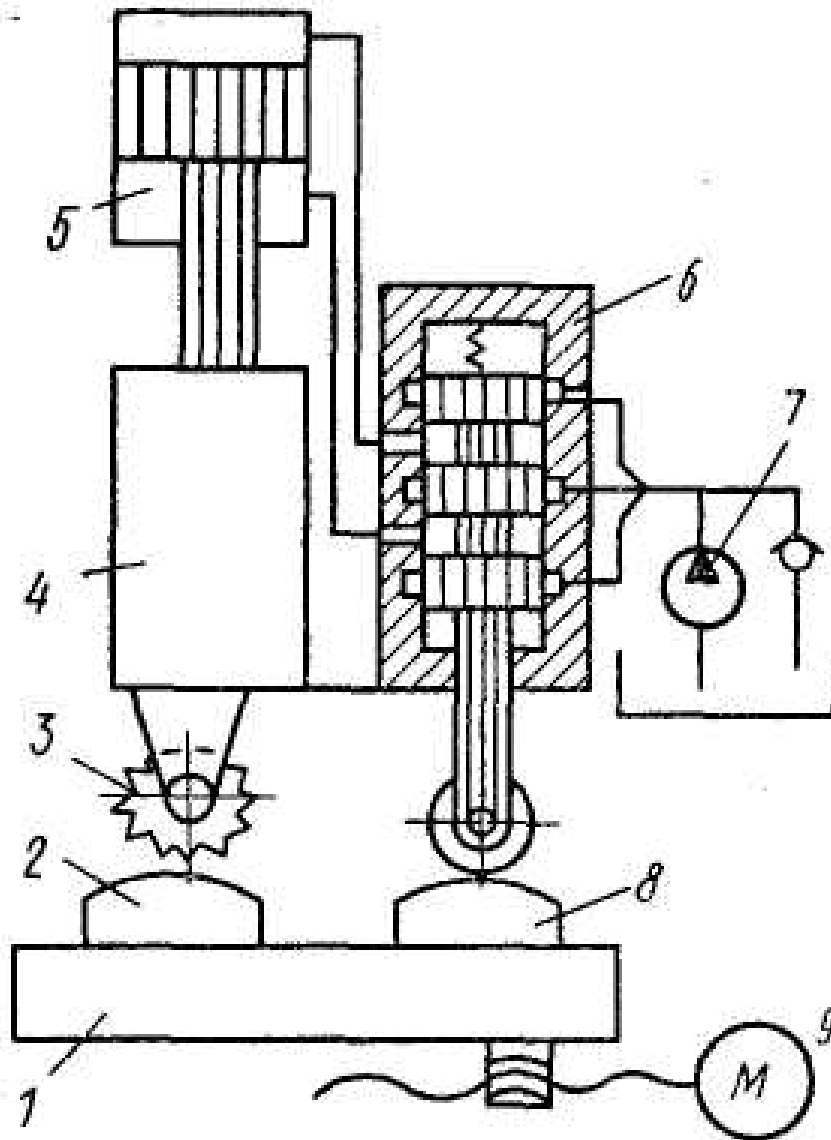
Принципиальная схема гидравлического следящего привода фрезерного станка: 1 – стол; 2 – заготовка; 3 – фреза; 4 – фрезерная бабка; 5 – шток цилиндра; 6 – следящий золотник; 7 – гидронасос; 8 – копир; 9 – электродвигатель
